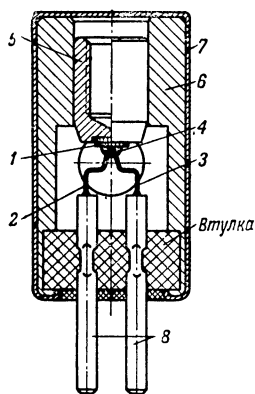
Устройство точечных триодов типов С1 и С2. 1 — германий; 2 — эмиттер; 3 — коллектор; 4 — заполнитель; 5 — держатель; 6 — корпус; 7 — кожух; 8 — вывод.
